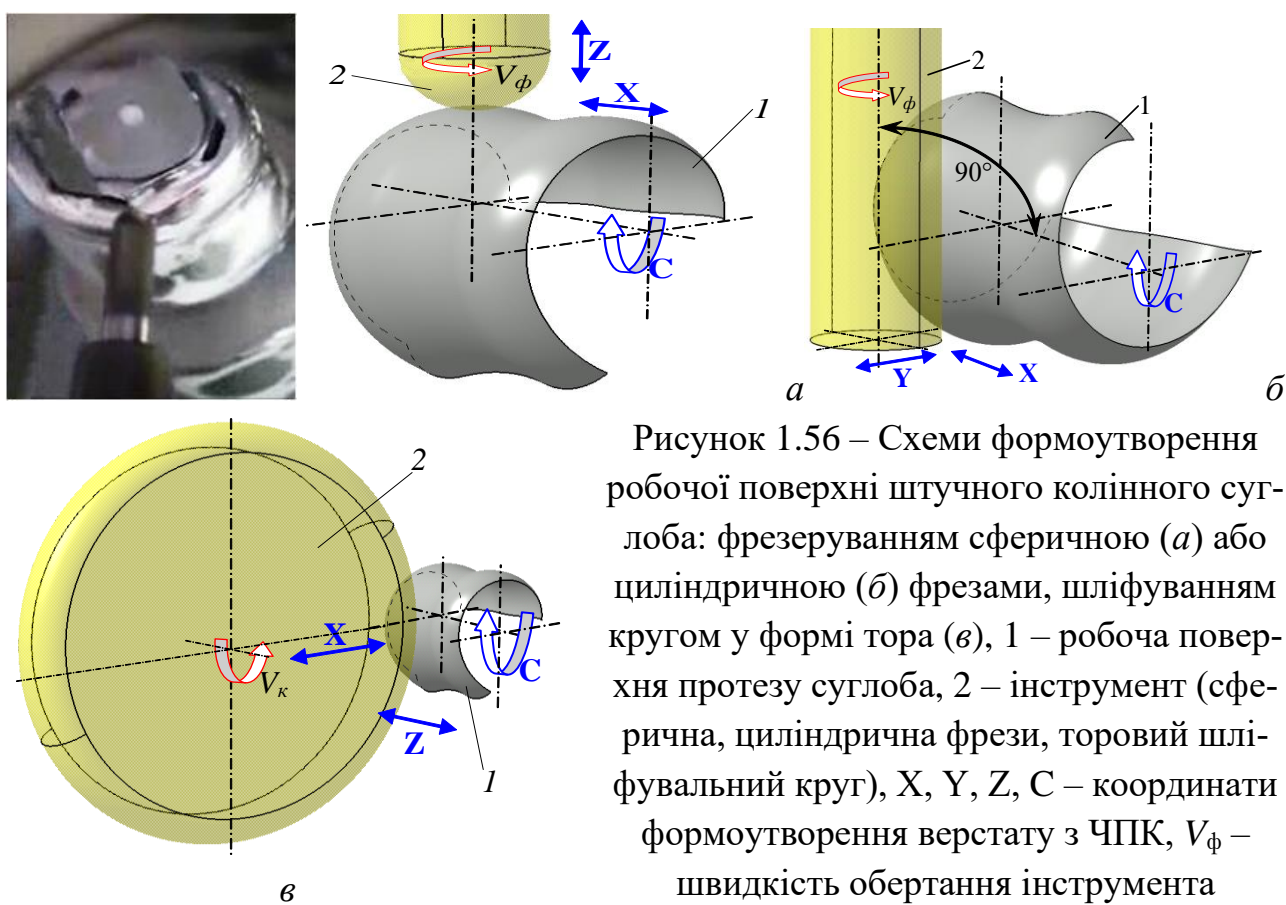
Схеми формоутворення робочої поверхні штучного колінного суглоба: фрезеруванням сферичною (а) або циліндричною (б) фрезами, шліфуванням кругом у формі тора (в), 1 – робоча поверхня протезу суглоба, 2 – інструмент (сферична, циліндрична фрези, торувий шліфувальний круг), X, Y, Z, C – координати формоутворення верстату з ЧПК,  $V_\phi$  – швидкість обертання інструмента
